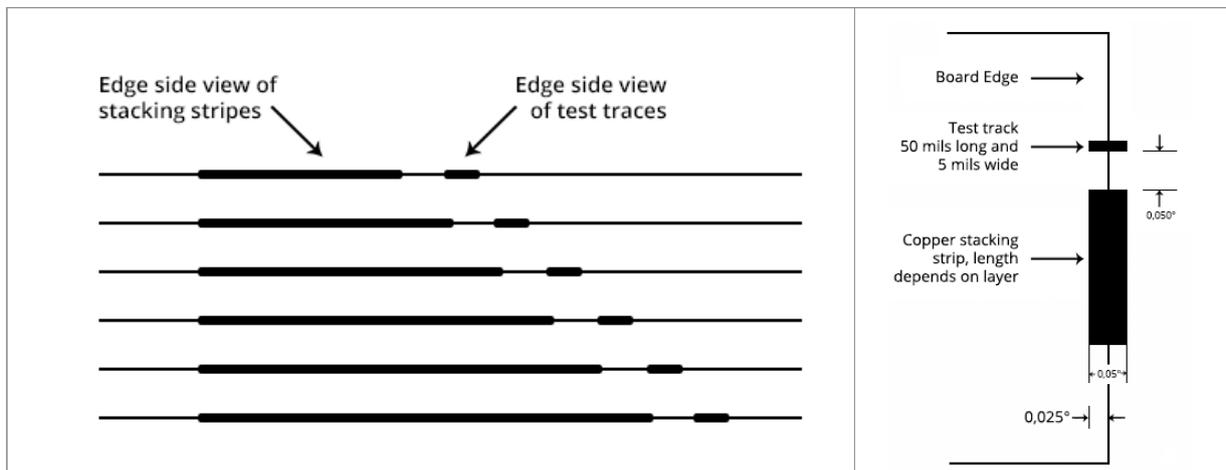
vista laterale delle strisce di sequenza e delle tracce test.
